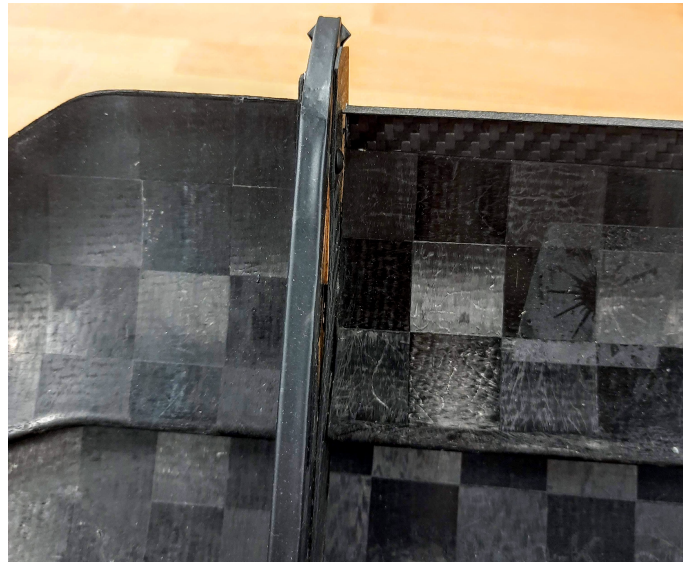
Detail spojovací desky v kontaktu s vnitřní bočnicí
